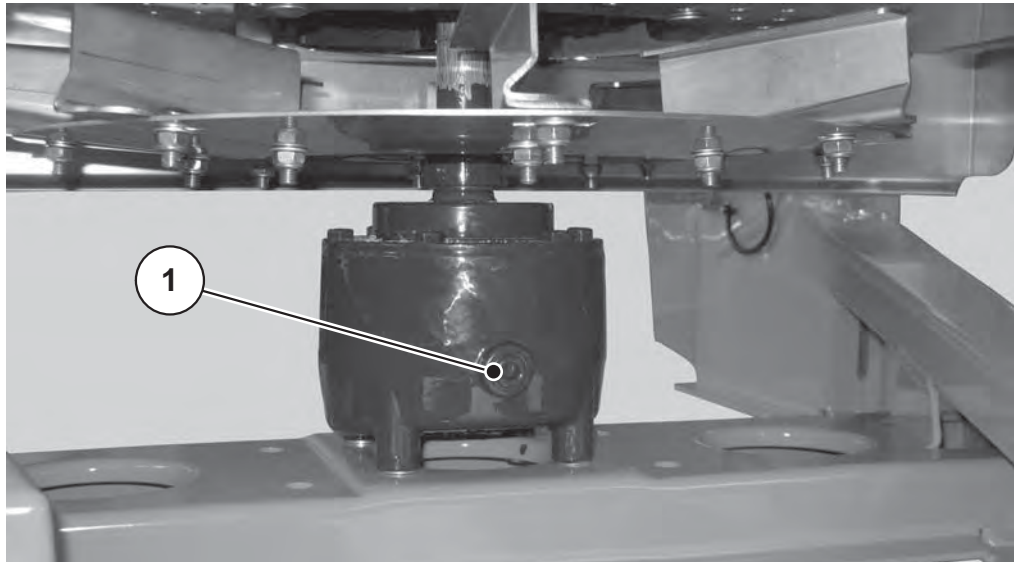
Kontrollschraube Ölstand Getriebeöl
